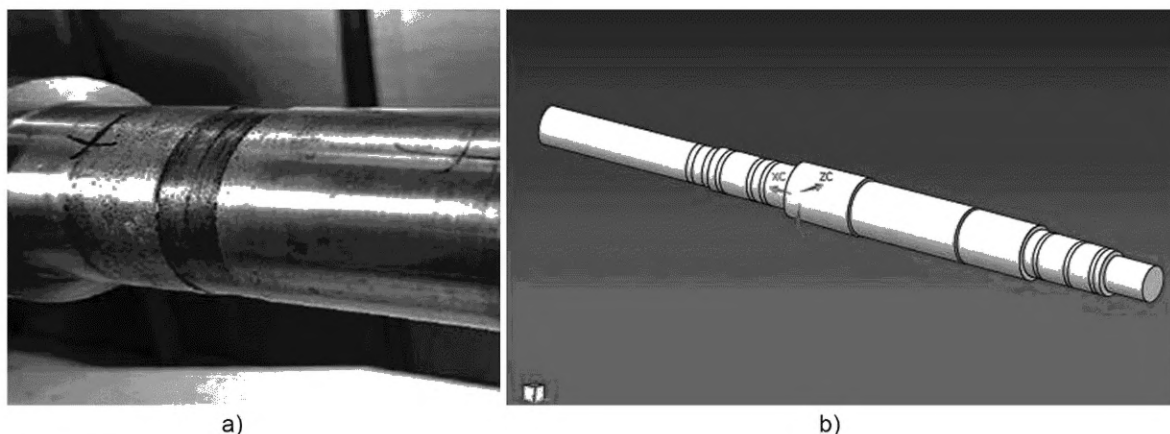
Вал подлежит восстановлению: а) пример изношенной области в месте расположения подшипника вдоль вала насоса; б) реконструированная CAD-модель
